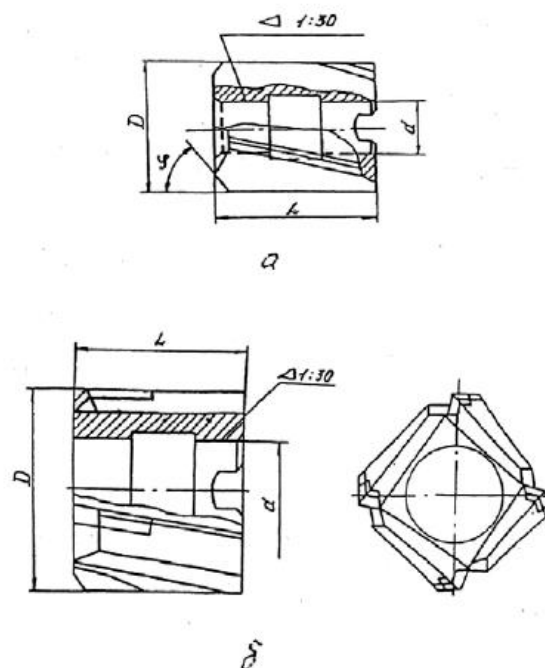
Конструкции насадных зенкеров: *а* – из быстрорежущей стали ГОСТ 5653–70; *б* – оснащённый пластинами из твёрдого сплава ГОСТ 3231–71
